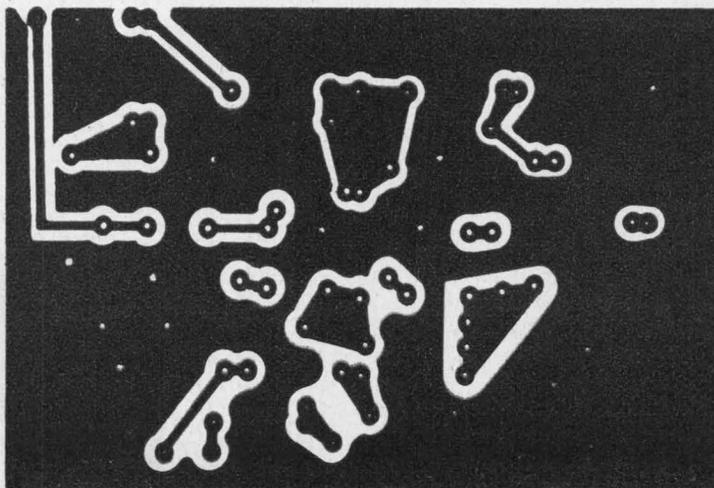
Face cobreada da plaqueta de circuito impresso utilizada para a montagem do O.F.V.
